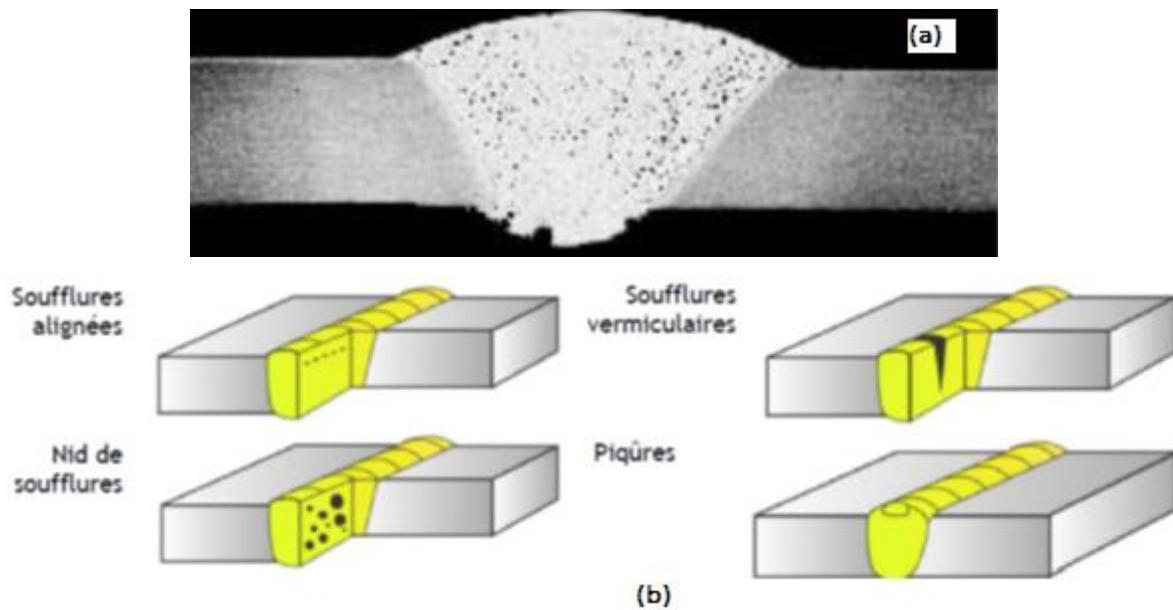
a) Porosité finement répartie dans une soudure TIG soudée t épaisseur 6 mm.[13]
